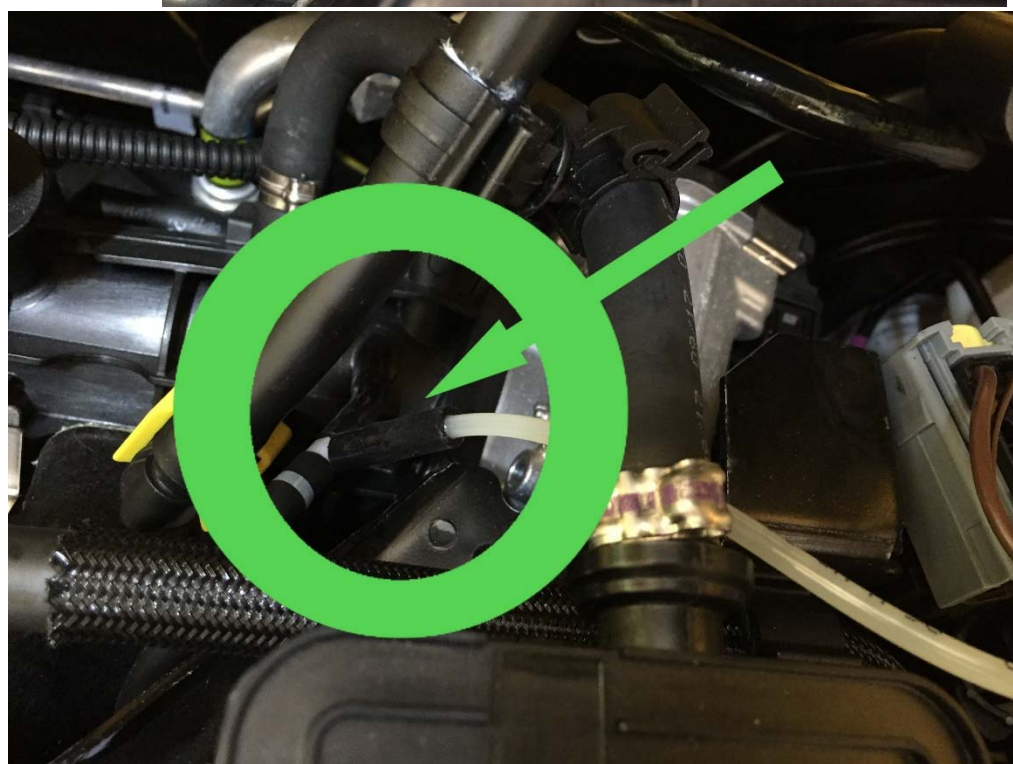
Inserire l'altro pezzo di tubetto nero e tubo in teflon sul raccordo a T.
